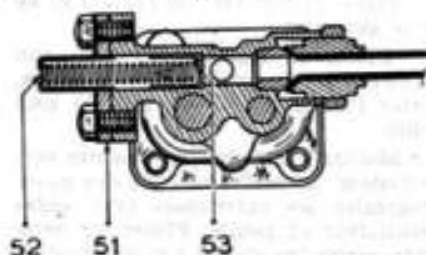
Vue en coupe du clapet de décharge à piston.
